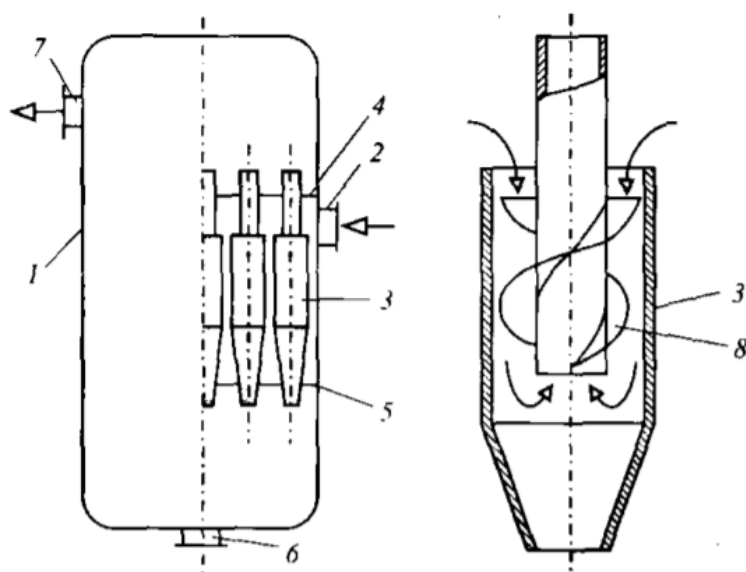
Циклонный пылеуловитель: 1 – корпус; 2 – ввод газа; 3 – корпус циклона; 4, 5 – перегородки; 6 – патрубок для удаления шлама; 7 – выход газа; 8 – винтовые лопасти
